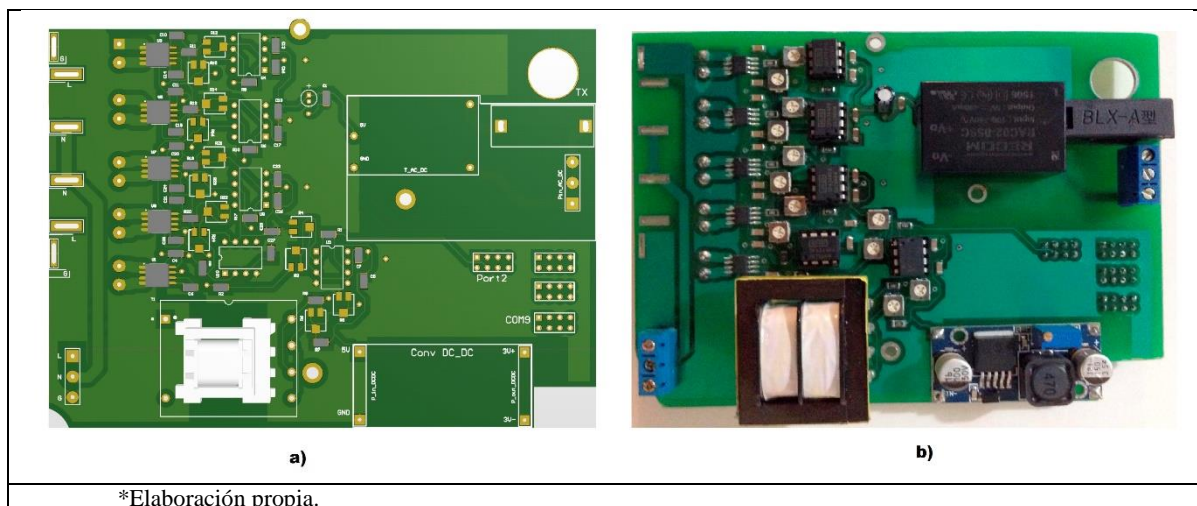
a) Modelo PCB b) Estructura PCB final (vista superior)
